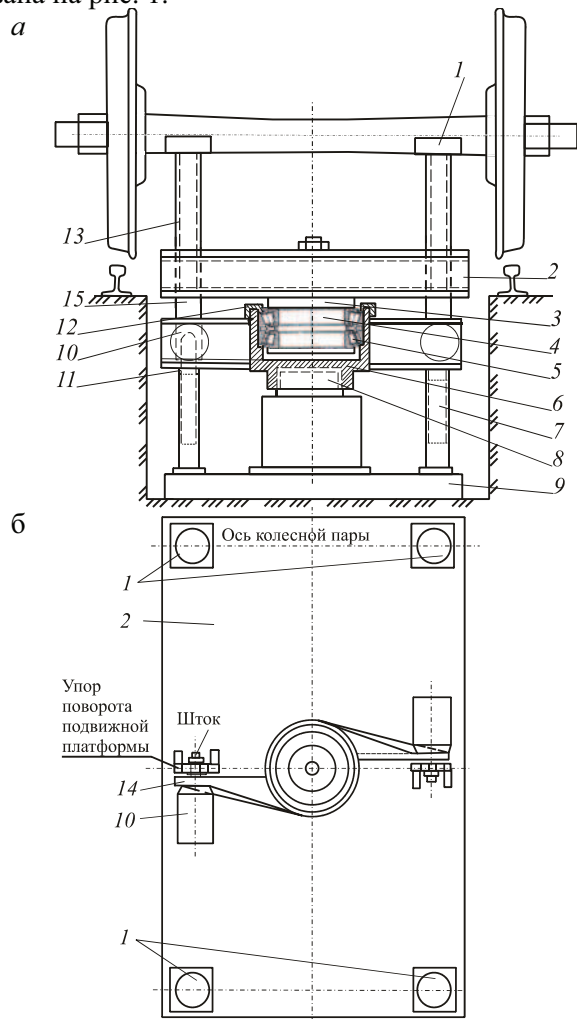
Общий вид стэнда и механизма нагружения для поворота тележки: 1 – винтовая опора; 2 – поворотная платформа; 3 – кольцо; 4 – вал; 5 – подшипник; 6 – обойма; 7 – направляющий стакан; 8 – домкрат подъема; 9 – фундамент; 10 – домкрат нагружения; 11 – направляющая; 12 – упор подшипника; 13 – винтовой стержень; 14 – стержень домкрата и месдоз; 15 – упорная пластина для передачи усилия от домкрата поворота поворотной платформе.
